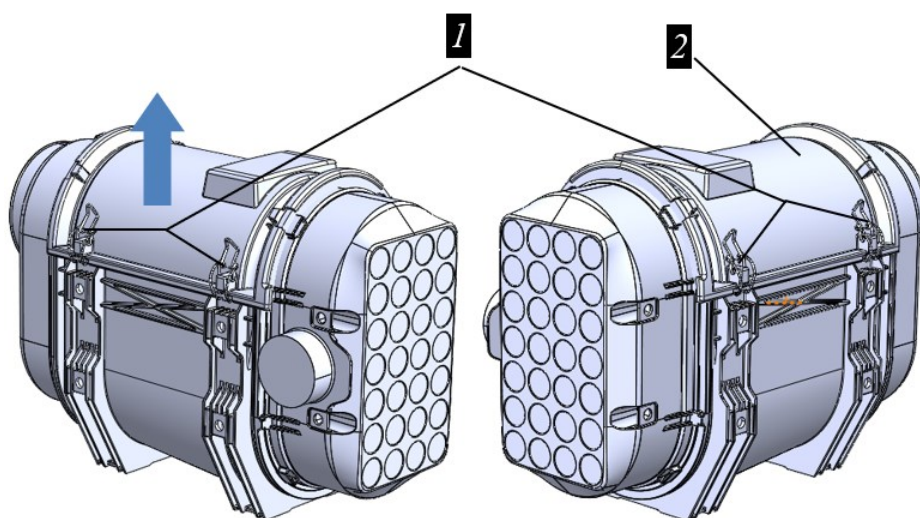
Корпус воздушного фильтра Тип 2
